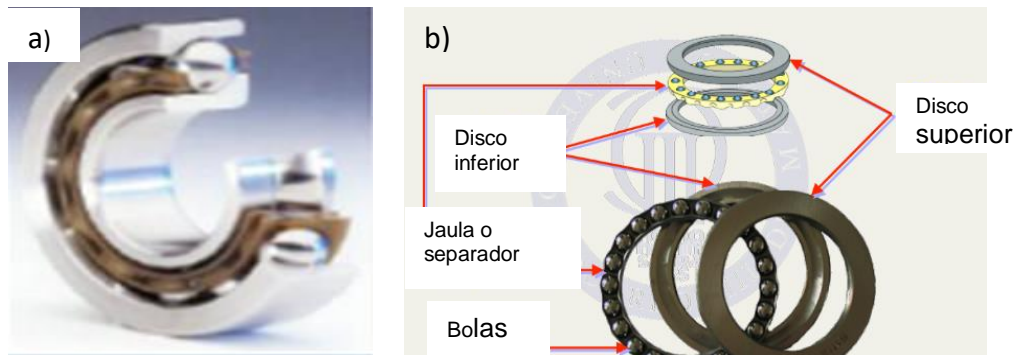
Rodamiento, a) recto tipo bolas; b) elementos internos [10].
